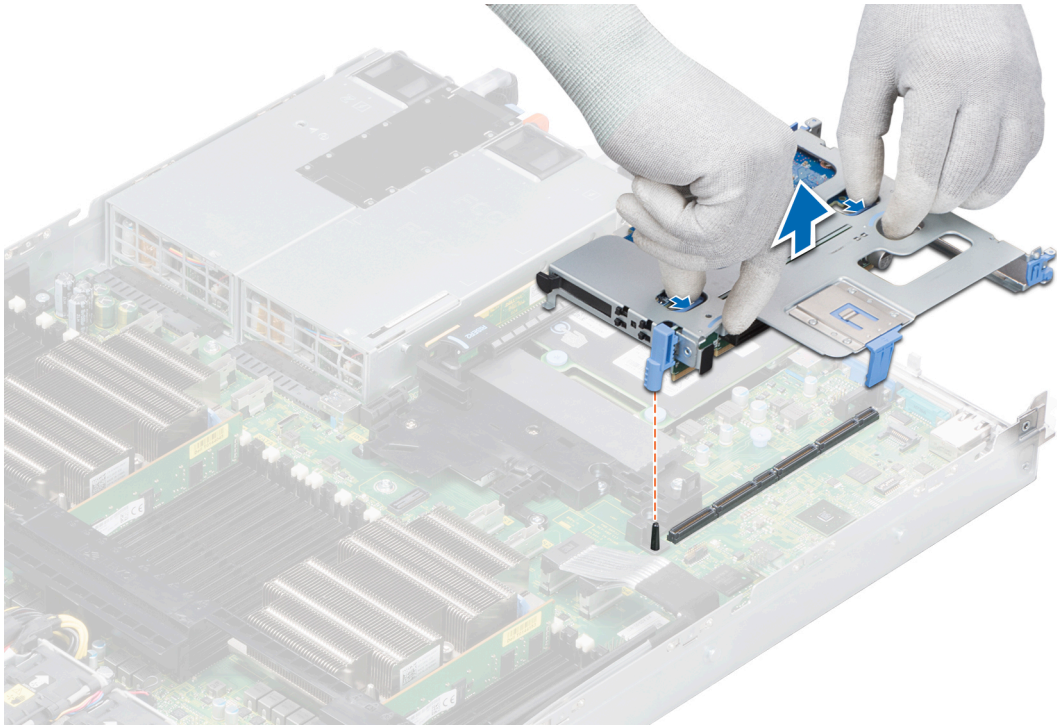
Retrait de la carte de montage pour carte d'extension 1
